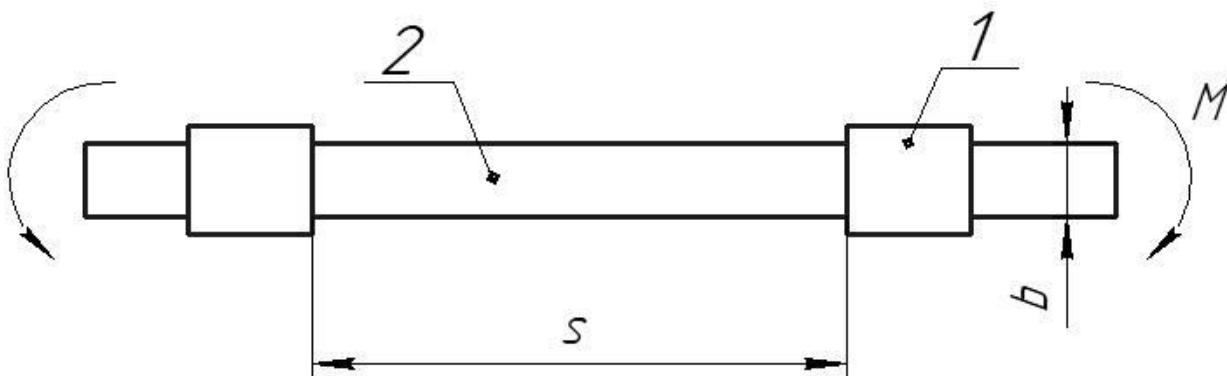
Модель чистого згину: 1 – модель інструменту за допомогою якого відбувається згин; 2 – заготовка, де: b – висота заготовки; s – відстань між інструментами; M – згинаючий момент
